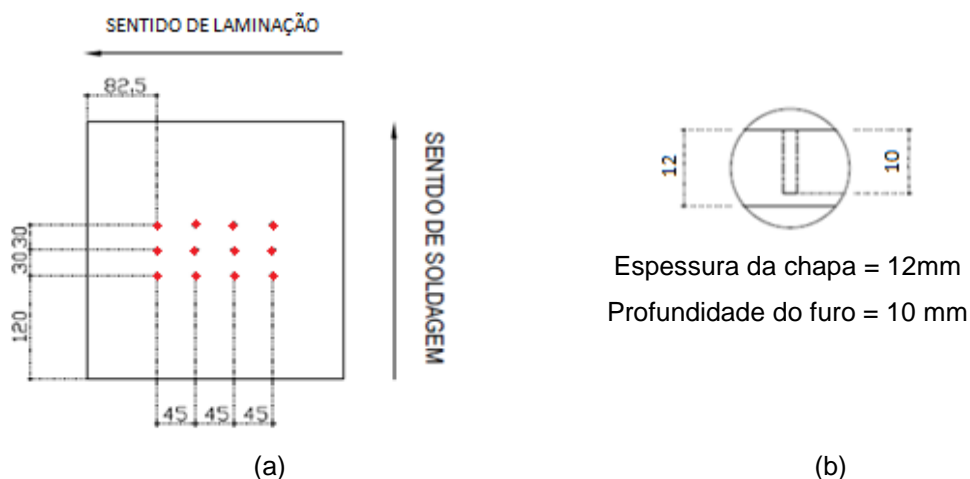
Representação esquemática das dimensões da chapa a ser soldada, com a localização dos furos para instalação dos termopares (a) vista inferior (b) detalhe do furo observado ao longo da espessura da chapa (unidade em mm)
